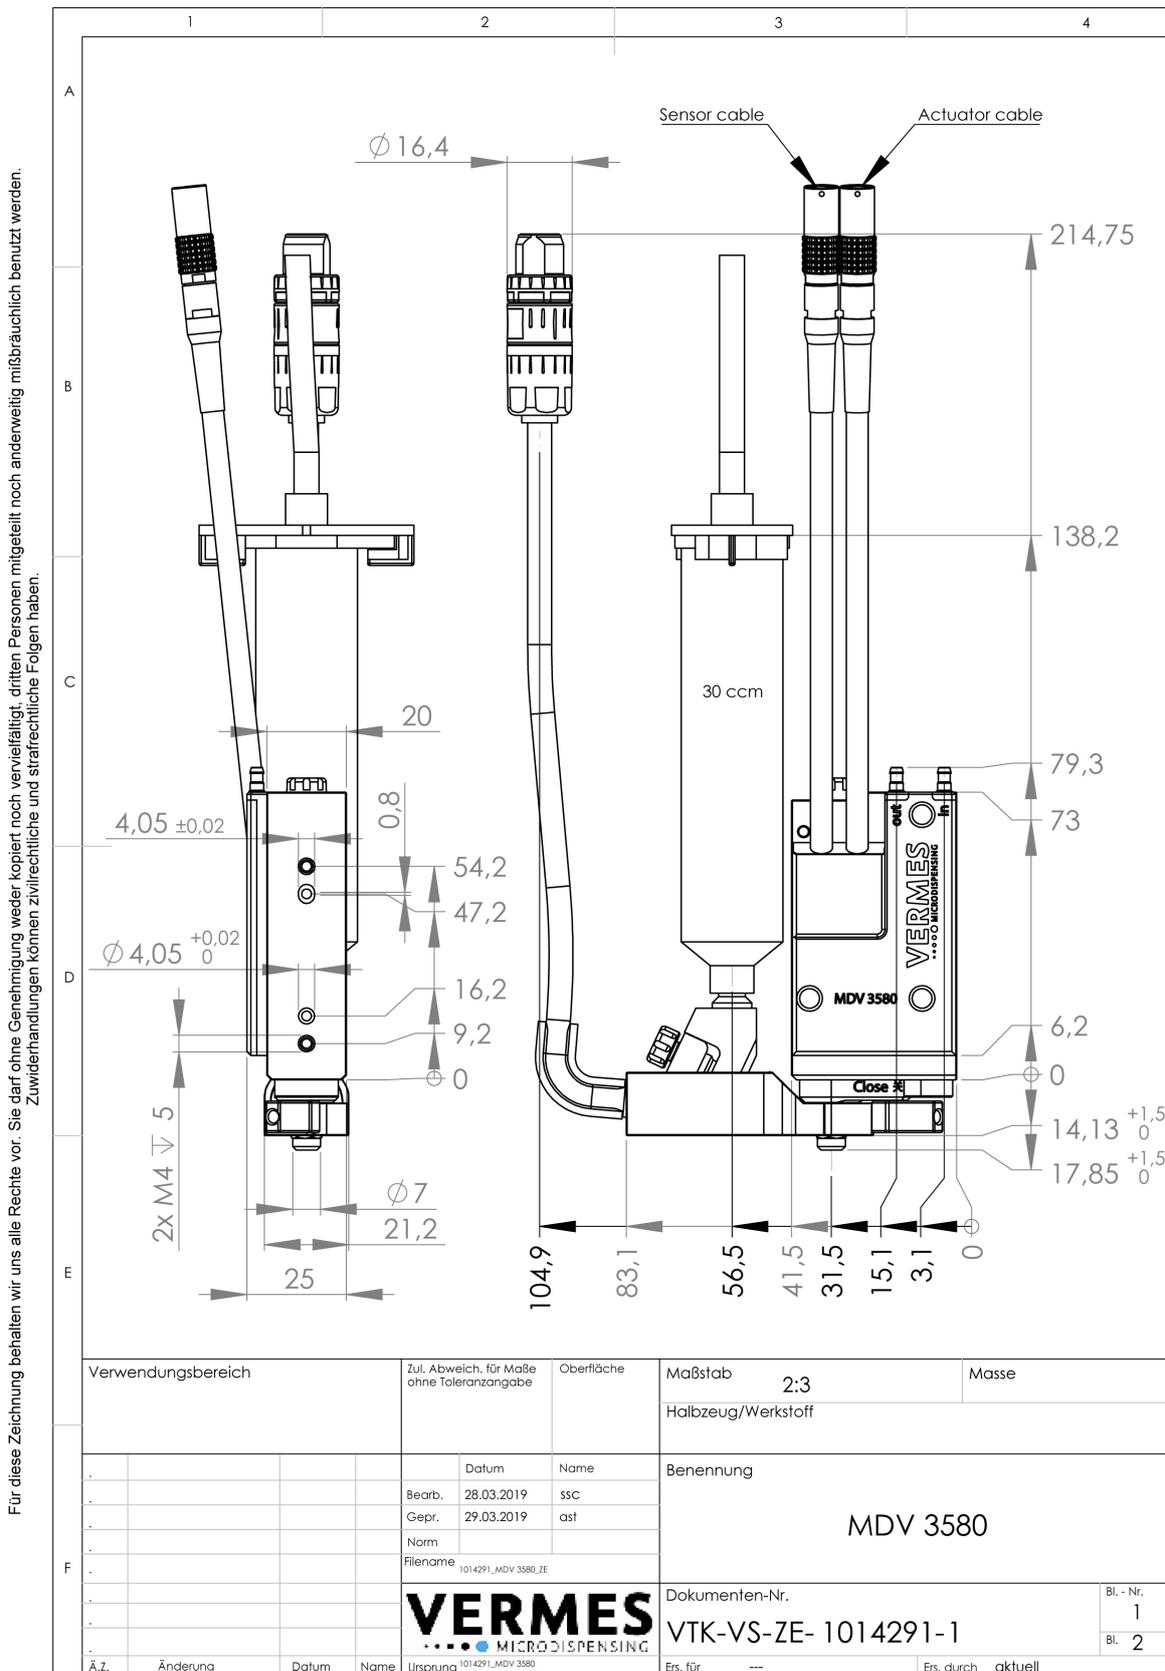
Maßzeichnung MDV 3580 frontal und seitlich
